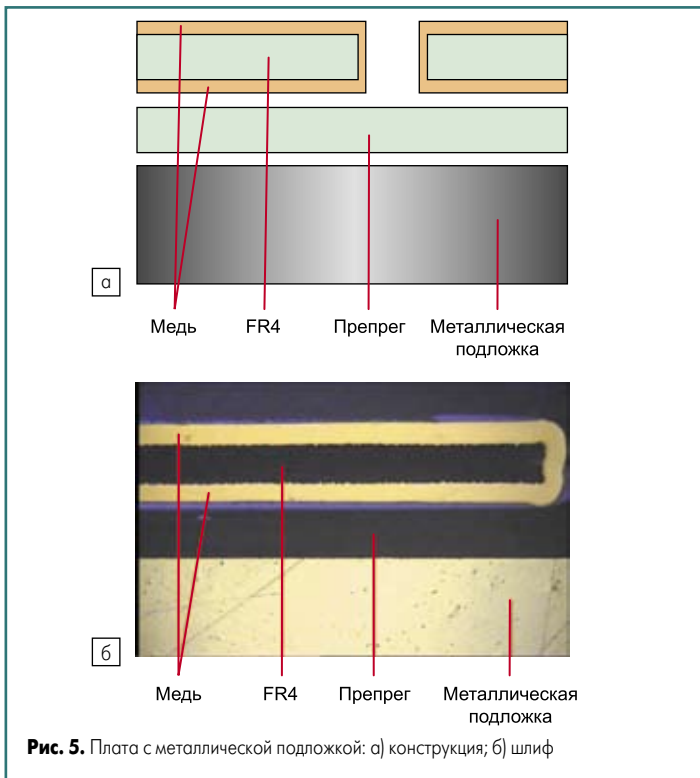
Плата с металлической подложкой: а) конструкция; б) шлиф
